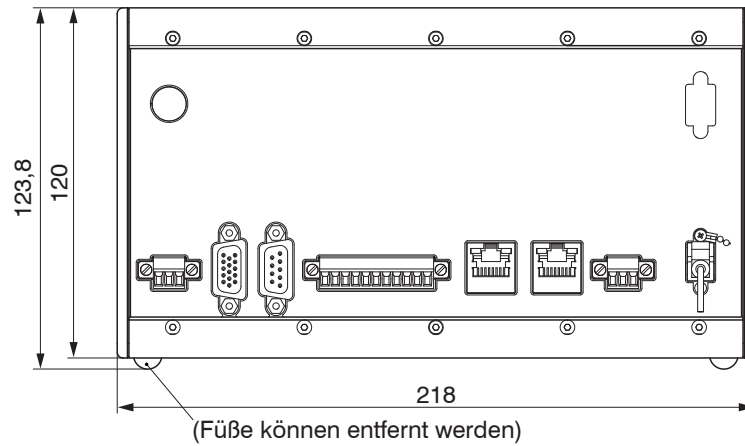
Maßzeichnung Frontansicht des Controllers IFC2421/2465, Abmessungen in mm
